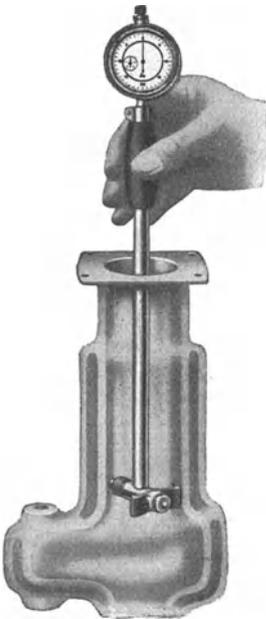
Fühlhebelmeßgerät zur Bohrungsmessung.
